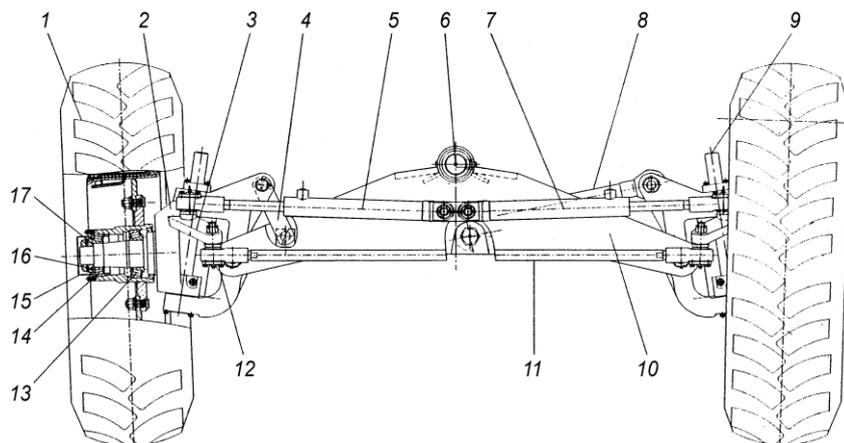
Передний мост автогрейдера ГС-14.03: 1 – колесо; 2 – поворотный рычаг с полуосью; 3 – кронштейн наклона колес; 4 – стяжка; 5, 7 – гидроцилиндры поворота колес; 6 – ось качания переднего моста; 8 – гидроцилиндр наклона колес; 9 – шкворень; 10 – балка; 11 – тяга; 12 – крышка шарового шарнира; 13, 14 – подшипники; 15 – крышка; 16 – замковая шайба; 17 – гайка
